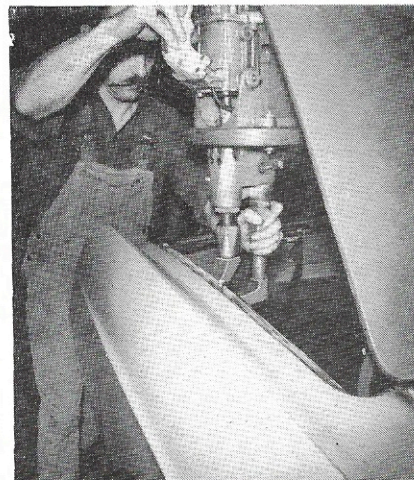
Soudage de l'aile arrière sur gouttière latérale. Pince ARO.
